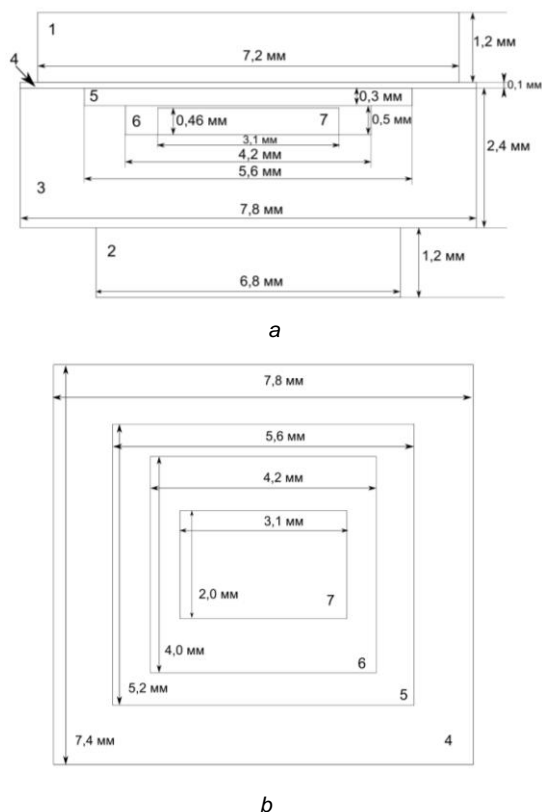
Вид модельного образца сбоку (а) и сверху (b): 1 — верхняя неполная защита WCu; 2 — нижняя неполная защита WCu; 3 — керамический корпус; 4 — крышка; 5 и 6 — монтажные площадки для установки кристалла Si; 7 — кристалл Si.
